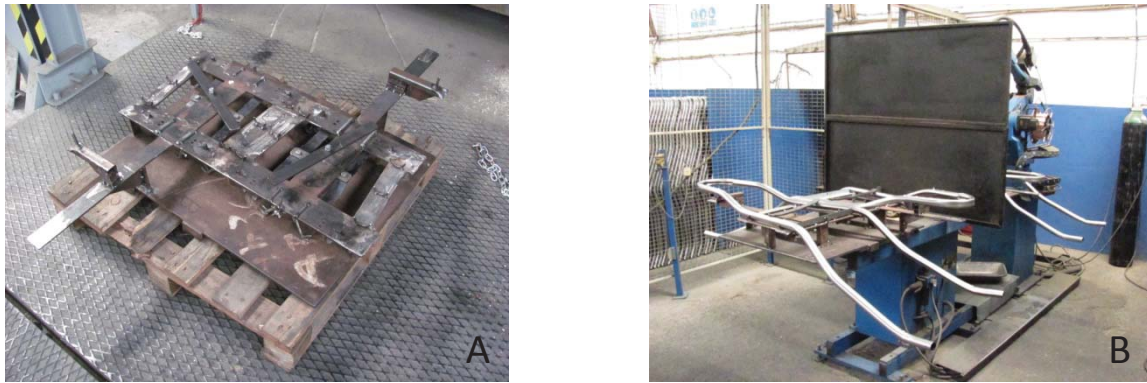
A – Gabarito para soldadura dos chassis no robot. B - Robot de soldadura em funcionamento.
